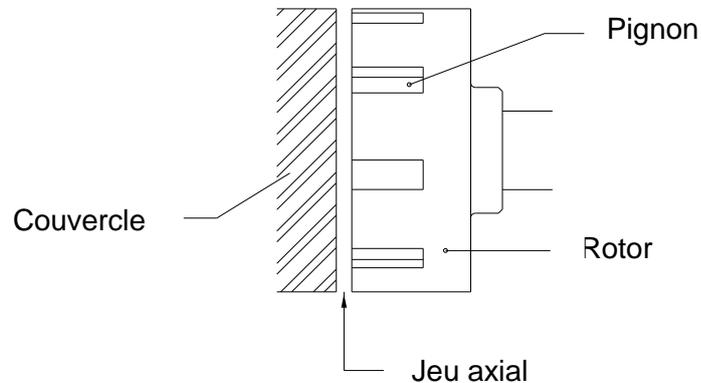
Jeu axial entre le rotor/pignon et le couvercle avant.
